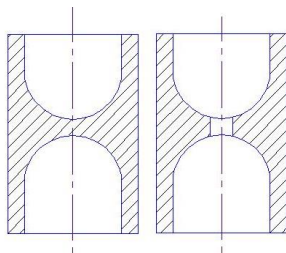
Полые детали с внутренними перемычками или с отверстием
